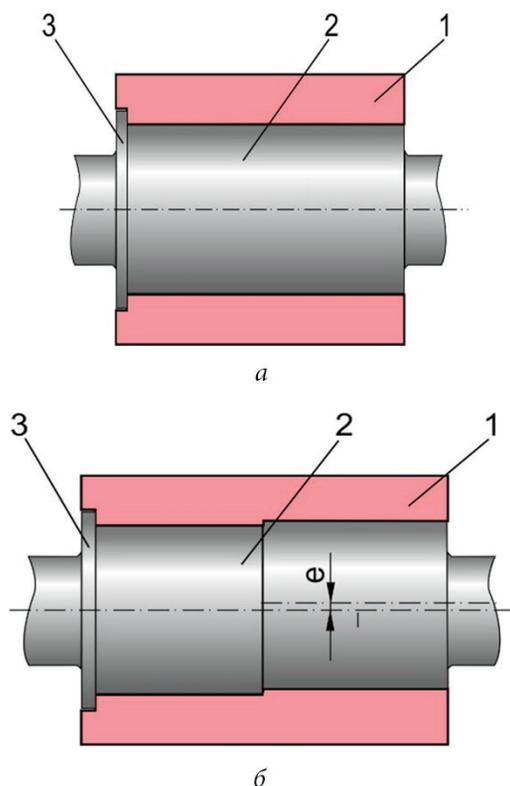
Конструкции соединения несущей оси (приводного вала) со ступицей:
